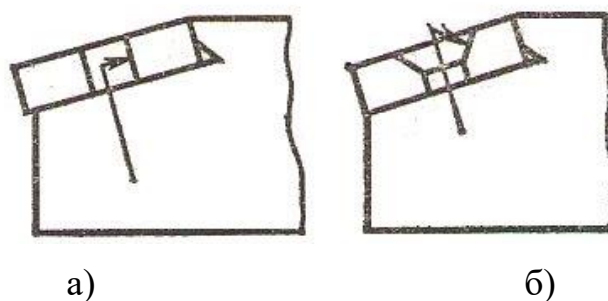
Схеми кріплення багатограних пластин в корпусі інструменту.
